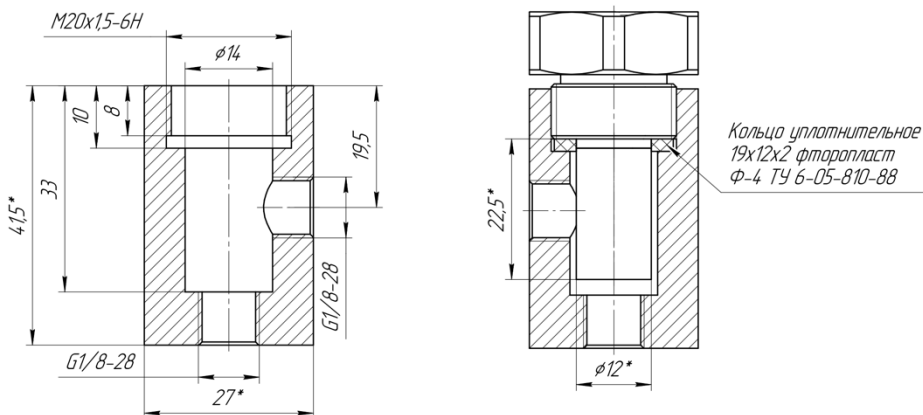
Конструкция проточной камеры для подключения измерительного преобразователя ДТР-3-Т20-М к газовой магистрали.
